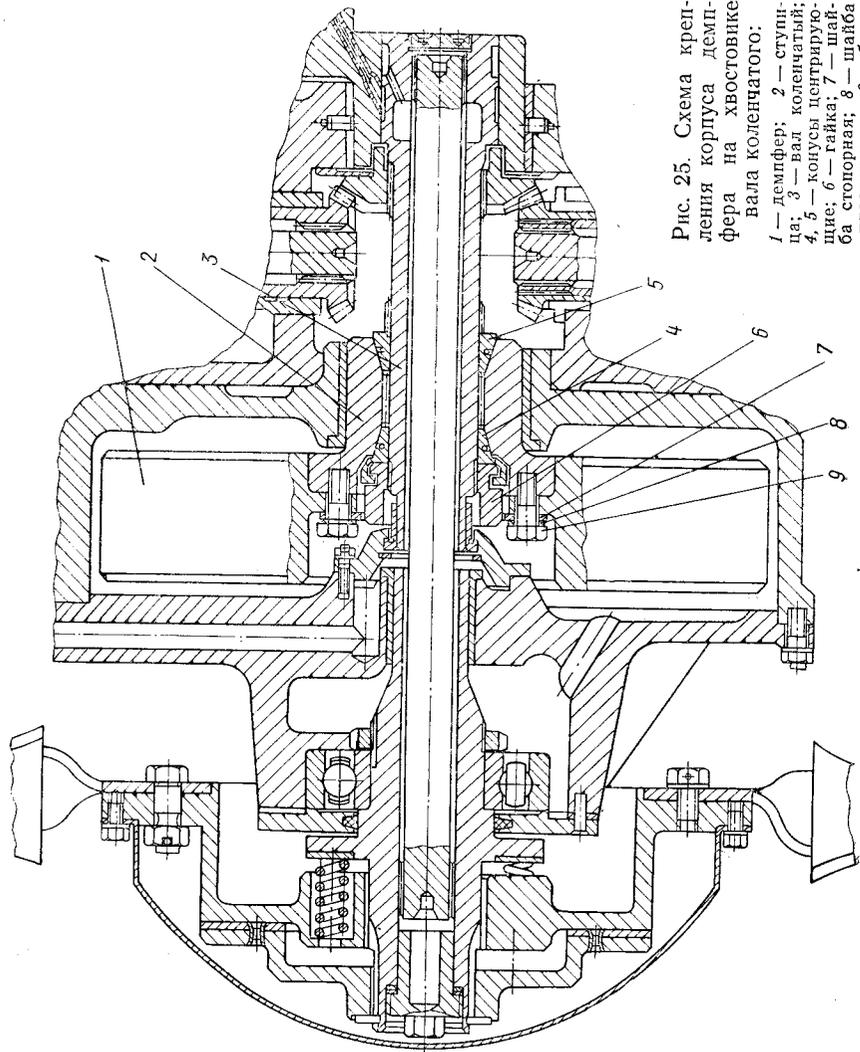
Схема крепления корпуса демпфера на хвостовике вала коленчатого:
